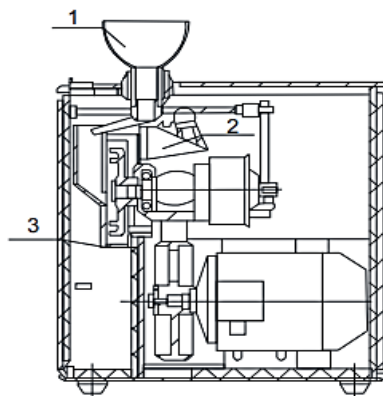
Схема лабораторного млина ЛМ-2: 1 — воронка; 2 — віброкоток; 3 — розмельна камера
